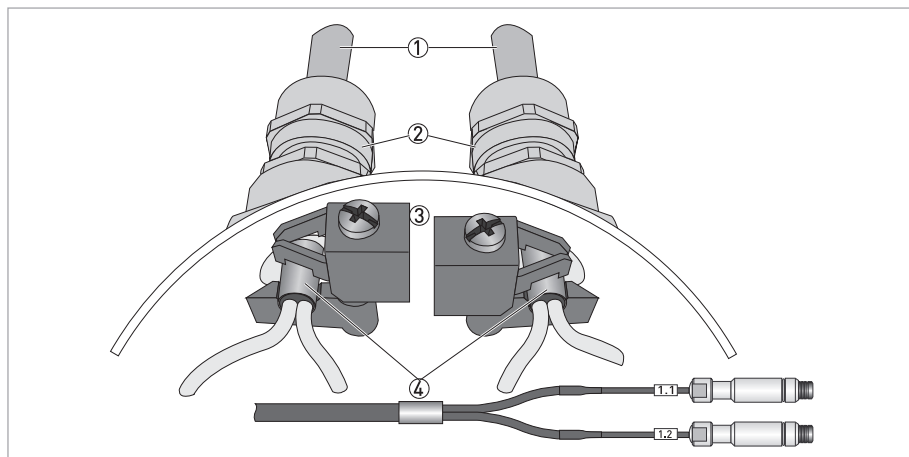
Befestigen der Kabel an der Abschirmbuchse.
